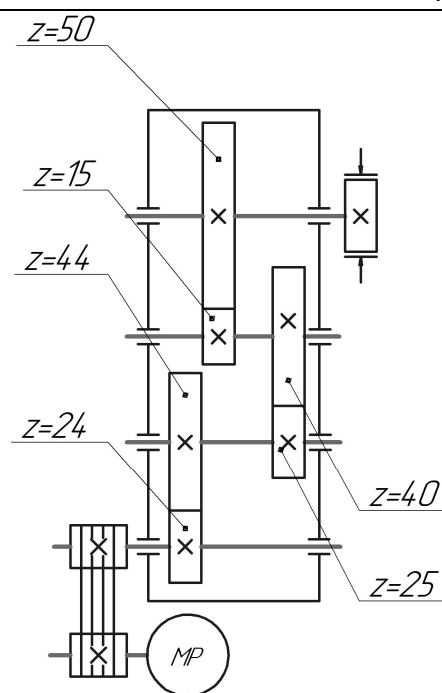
Кинематическая схема исследуемого горизонтального редуктора
